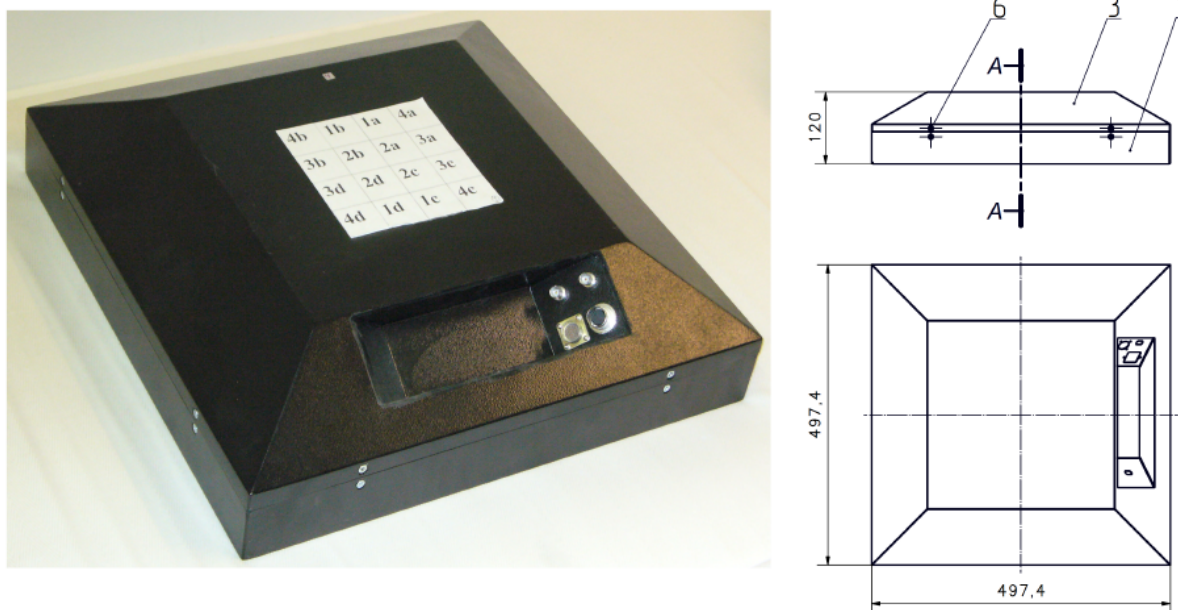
Фотография детектора SC16 и его габаритный чертеж.
